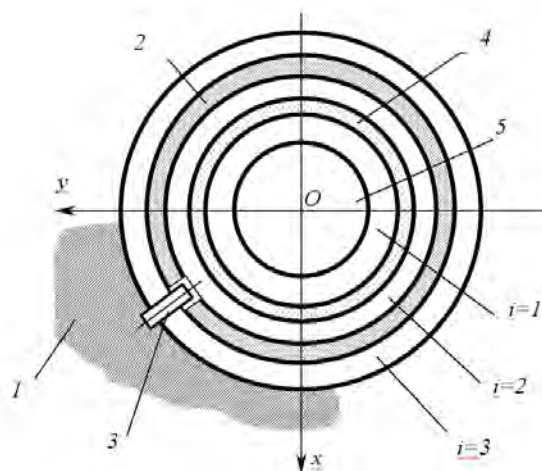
Схема трехслойного подшипника: 1 – корпус; 2 – ПН моноштулка; 3 – ограничительный штифт; 4 – ПВ втулка; 5 – ротор
